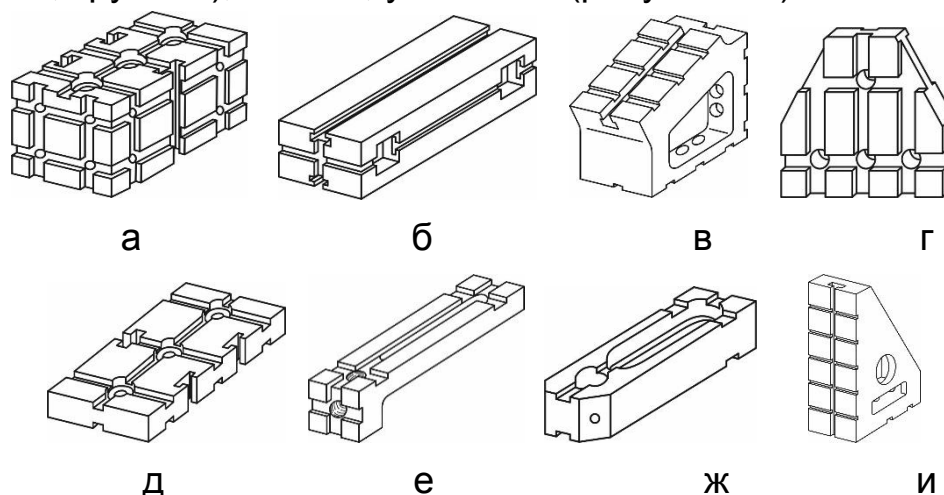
Примеры корпусных деталей: а, б – опоры; в – опора угловая; г, д, е – прокладки; ж – планка; и – угольник
